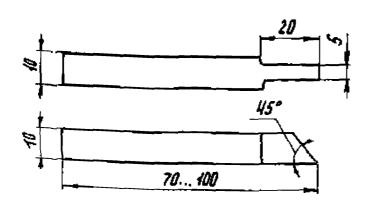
Боек для изготовления искусственных дефектов тила зарубок
